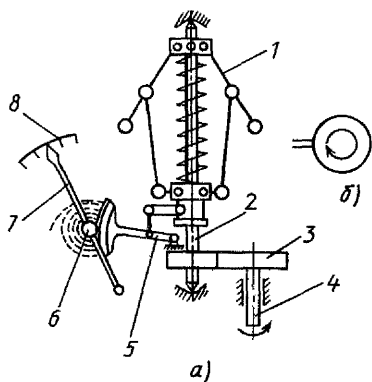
Центробежный тахометр: а — схема; б — условное обозначение
